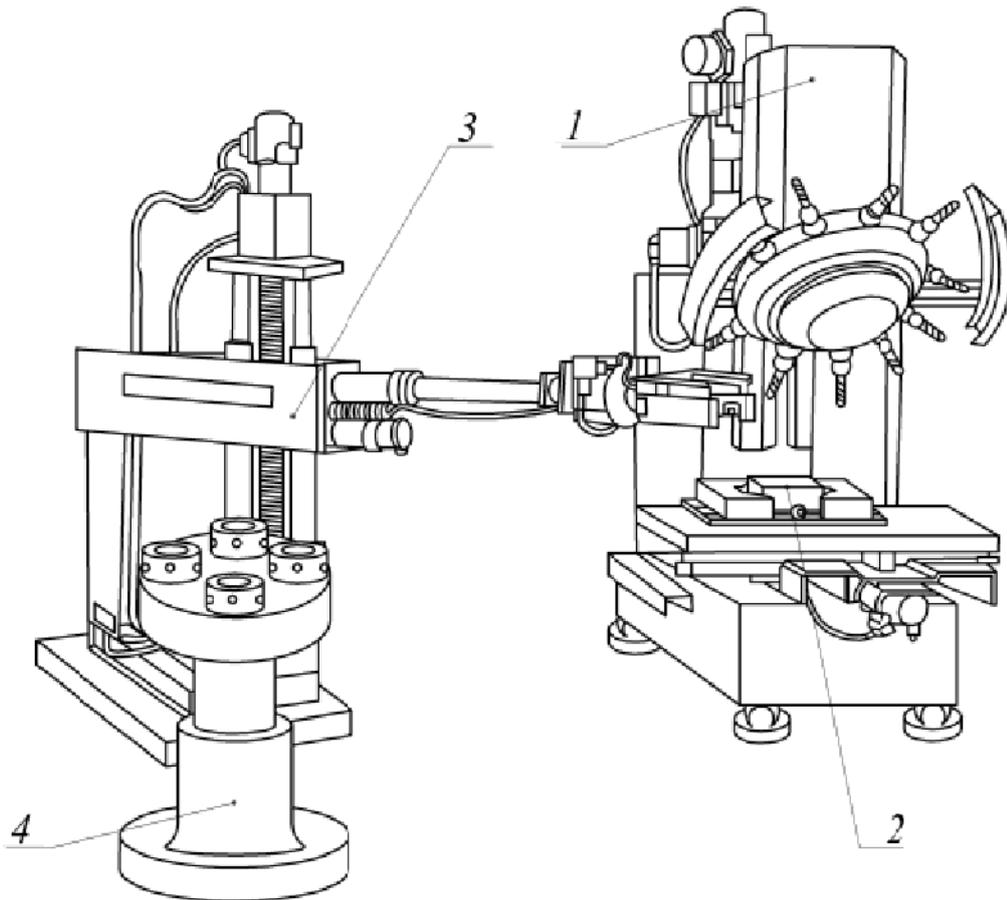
Автоматизоване робоче місце для фрезерної обробки
